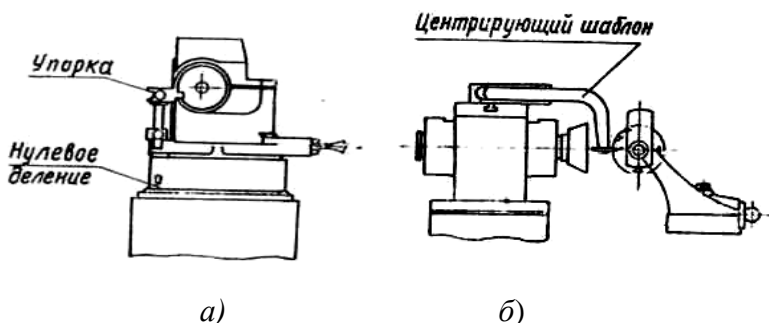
Установка упорки (а) и шаблона (б) при заточке спиральных фрез
